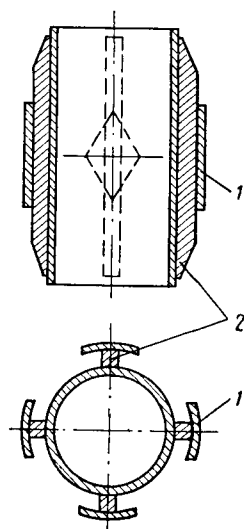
Центрирующий фонарь конструкции АзНИИ.
